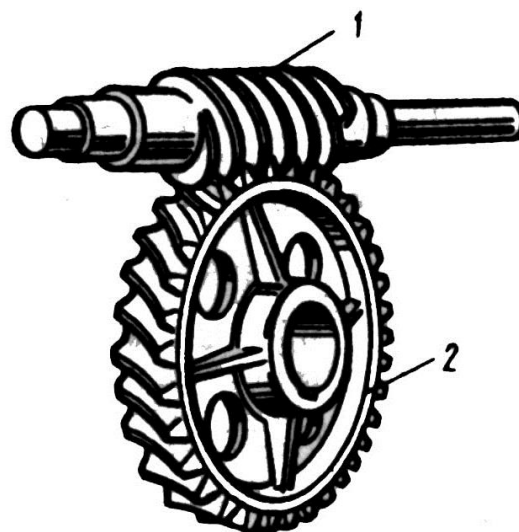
Червячная передача: 1 – червяк; 2 – венец червячного колеса
